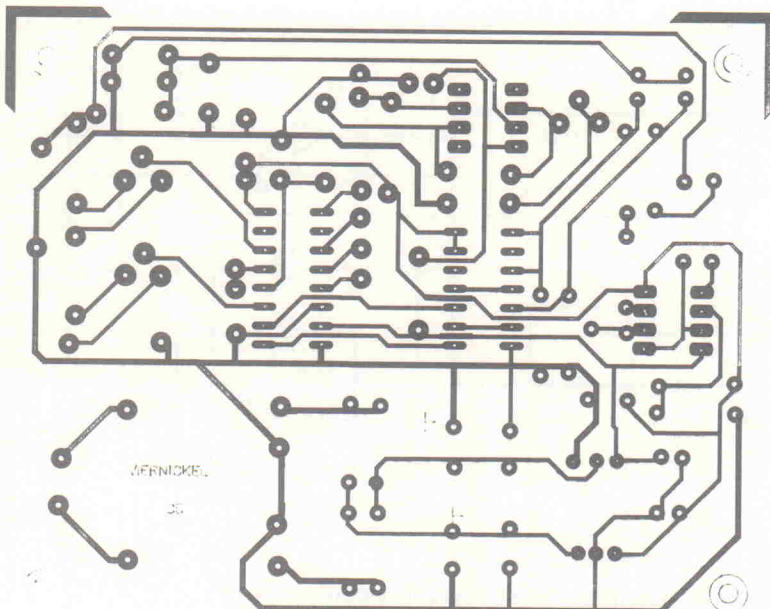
Alles auf einer Platine: das Layout für den Umschalter.
